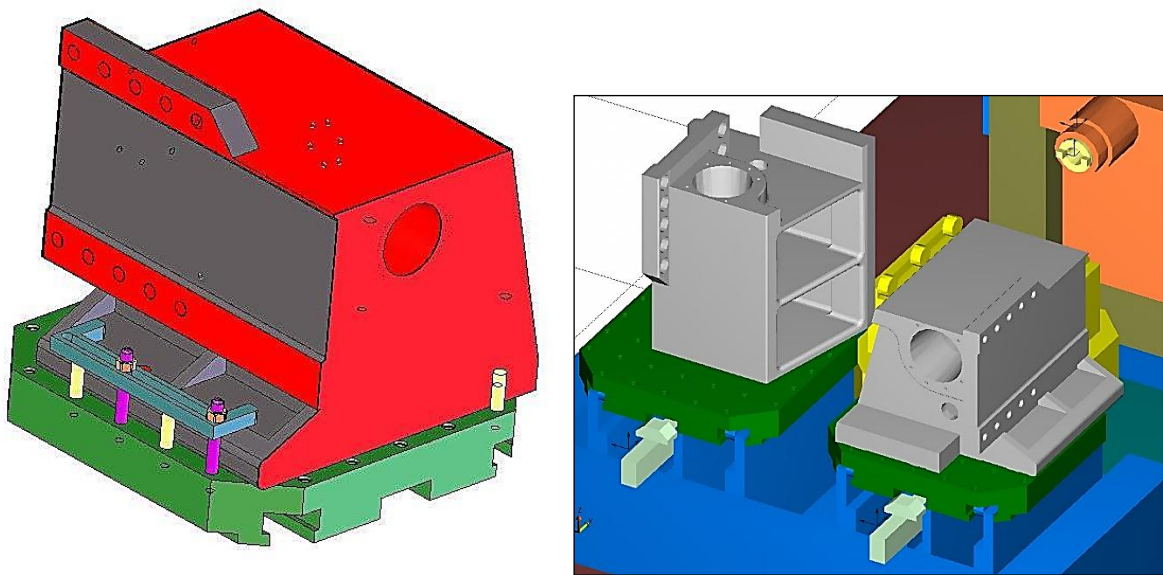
УЗП для обробки деталей типу «Корпус центральної бабки»
